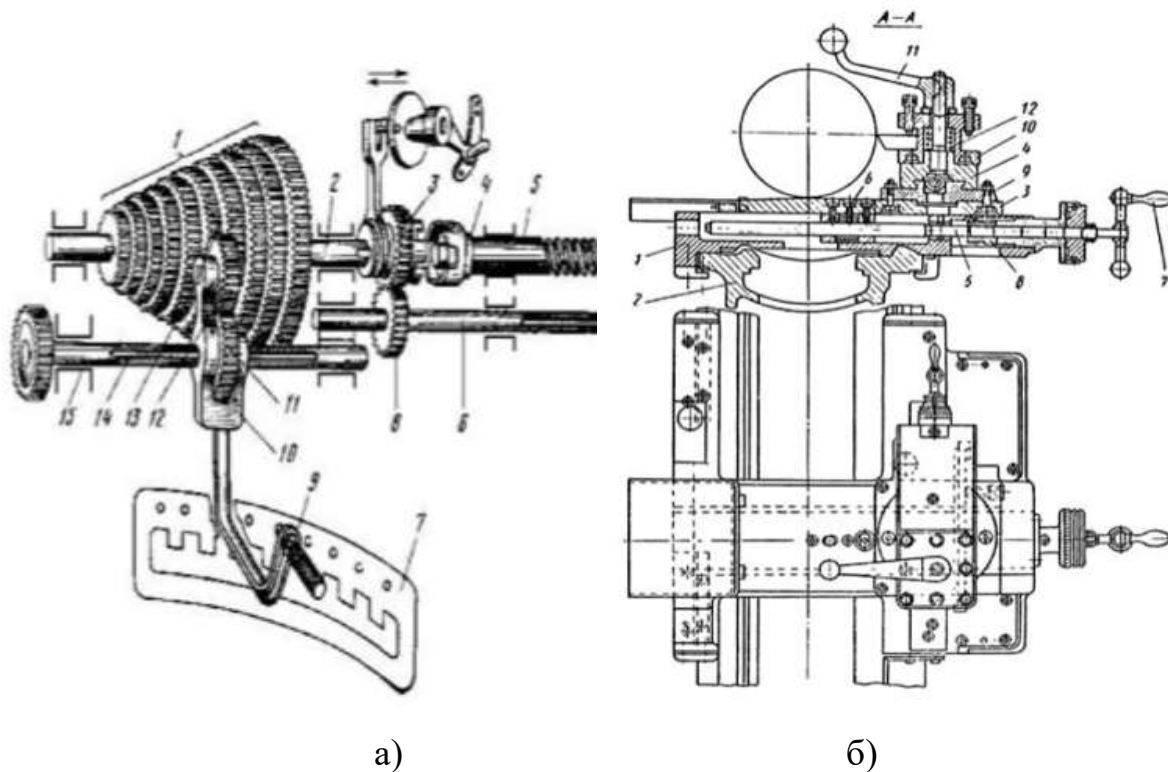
Механізм Нортонa коробки подач токарного верстату 1К62 (а) та супорт (б)
